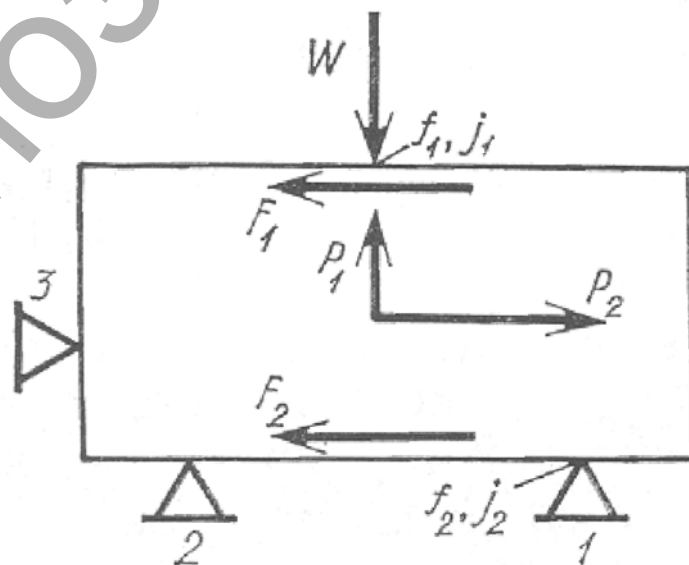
Схема установки заготовки и схема действующих на нее сил
